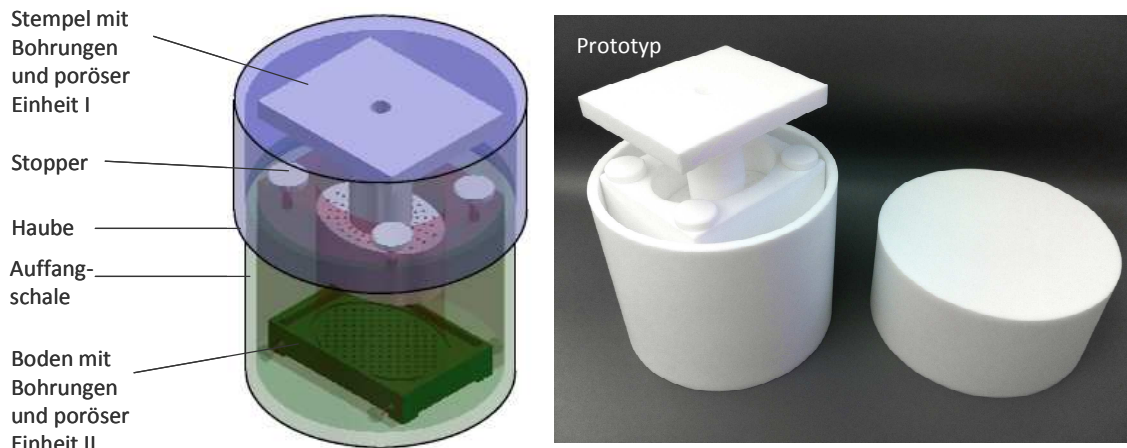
Reaktor - Technische Zeichnung und Prototyp aus PTFE
